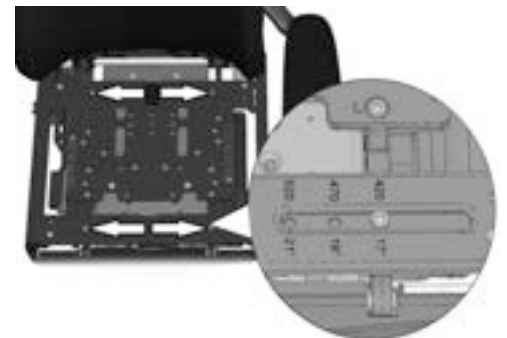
Die Sitzbreite ist mit vier Schrauben fixiert.
